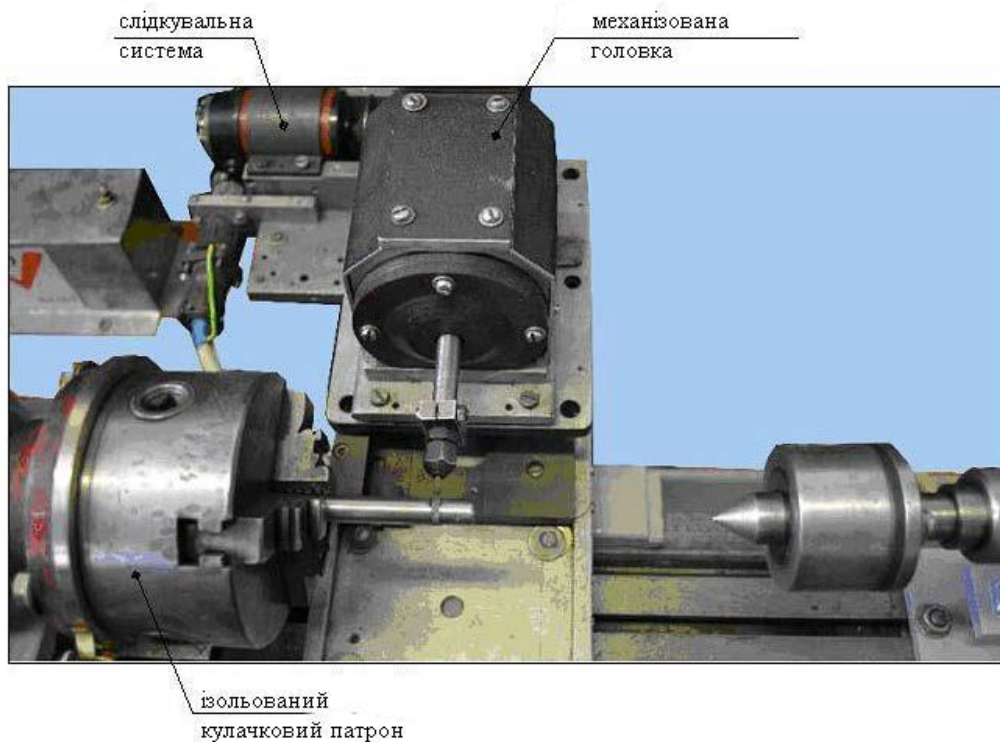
Робоча зона механізованої установки ІМЕІ-1001-ІМЕС
